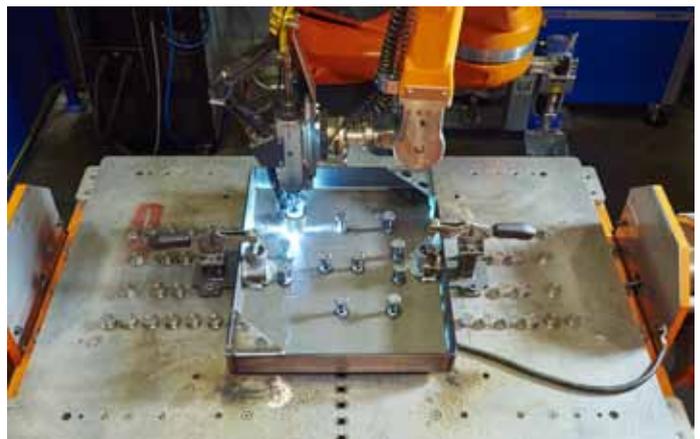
Die neue Schweißanlage kombiniert Bolzen- und Lichtbogenschweißen in einem System.
